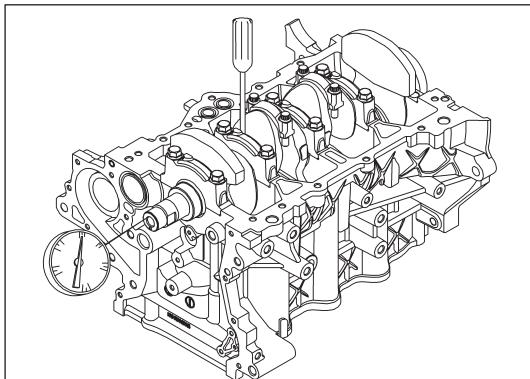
Измерение осевого зазора коленчатого вала
